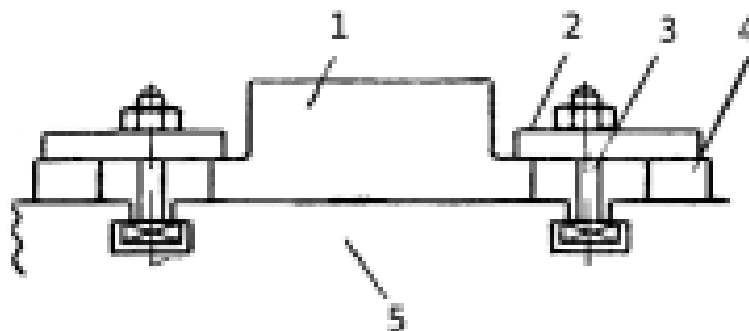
Прижимные планки: 1 — заготовка; 2 — прижимные планки; 3 — болты; 4 — подкладки; 5 — стол станка.
